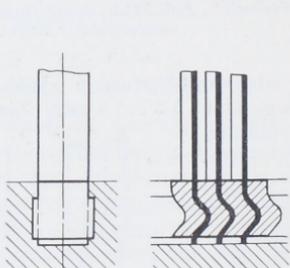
Befestigung der Brüner Maschinenfabrik.
